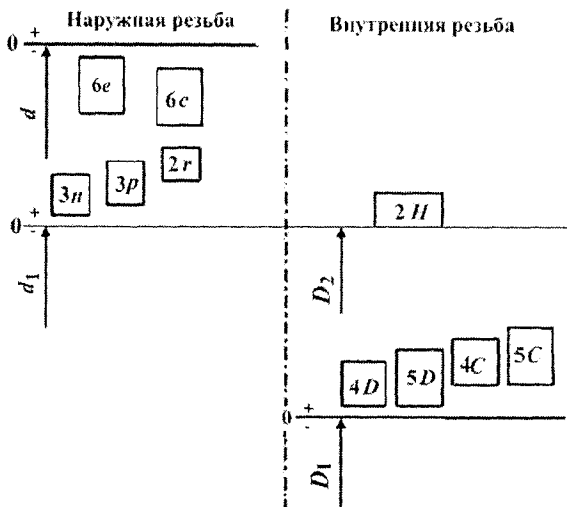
Поля допусков метрических резьб для соединений с натягом
